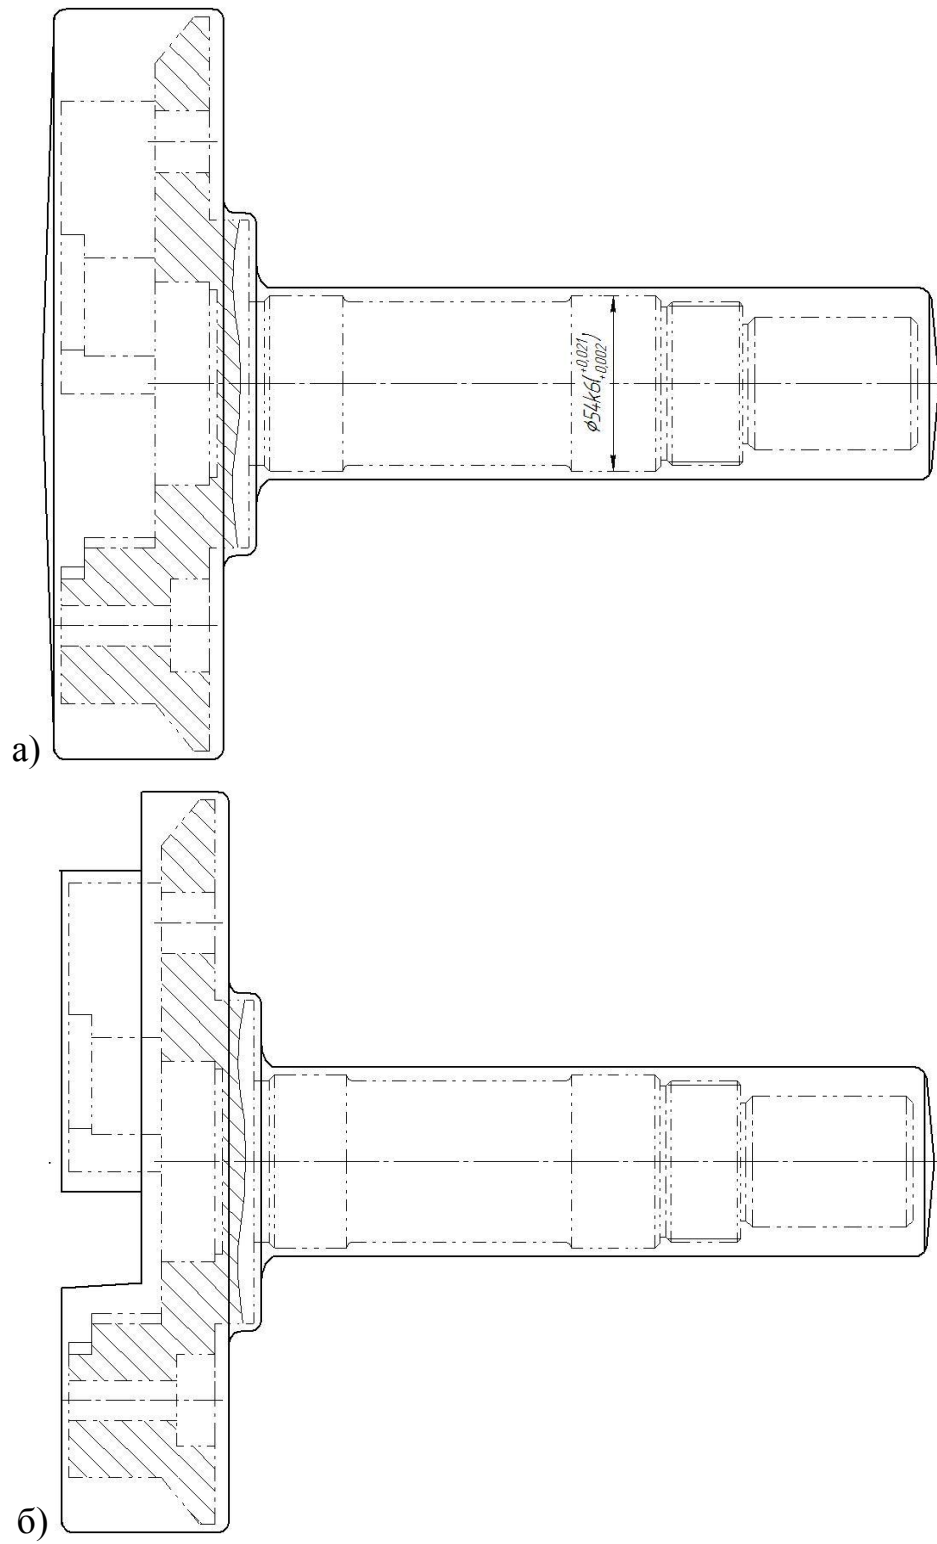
Эскизы заготовок: а) штамповка, б) отливка
